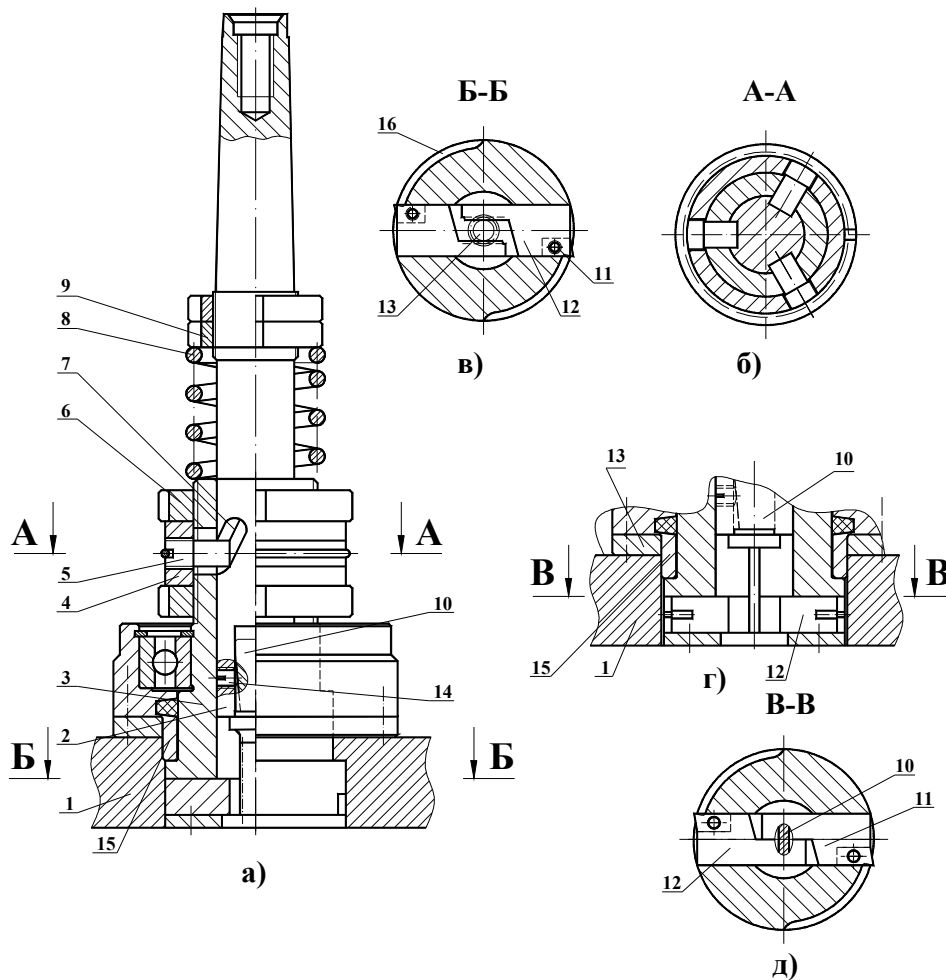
Пристрій для розточування кільцевих канавок в отворах корпусних деталей з використанням кінематичних зв'язків оправка-різець з'єднань: а, б) рейкове; в, г) кулачкове, д) еліпсне
